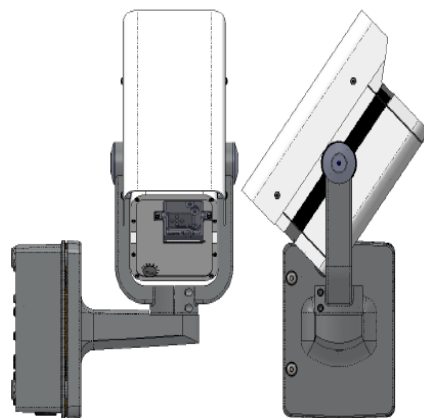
Ejemplo de orientación: la cámara ha girado 90 grados hacia la izquierda y apunta 50 grados hacia arriba
